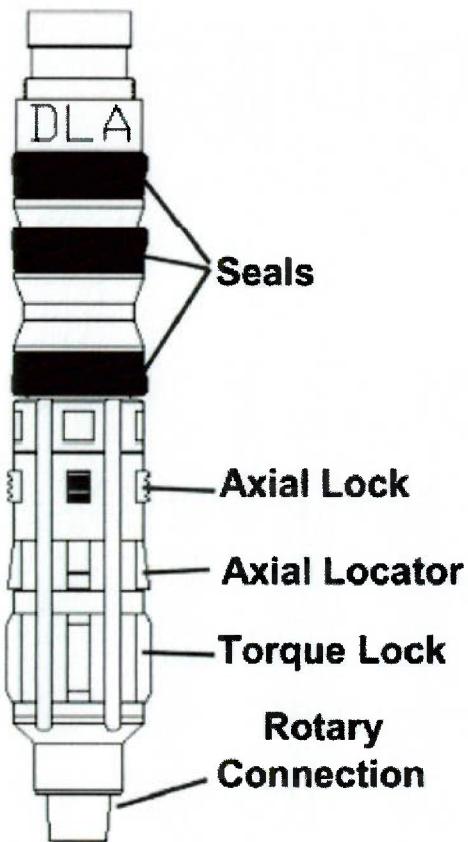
Drill Lock Assembly. Fonte: Warren et al. (2003)
